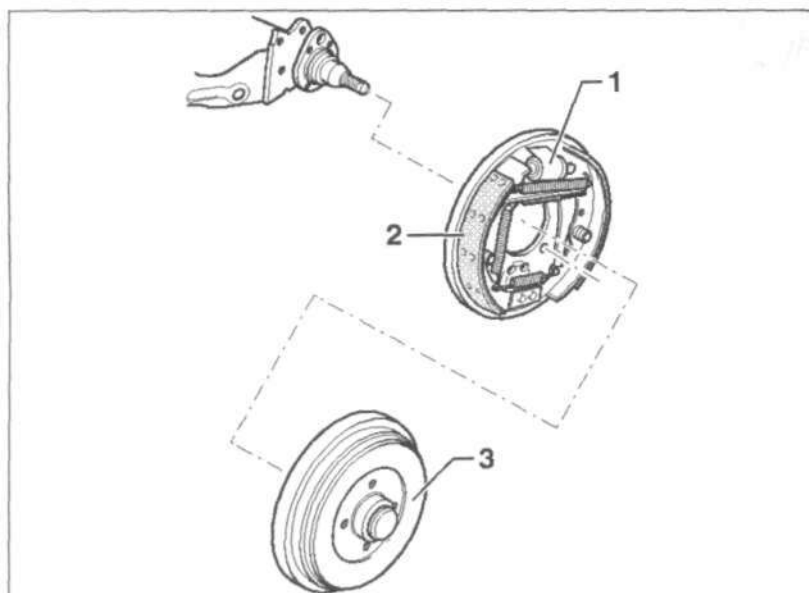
Автомобили с задними барабанными тормозными механизмами:
